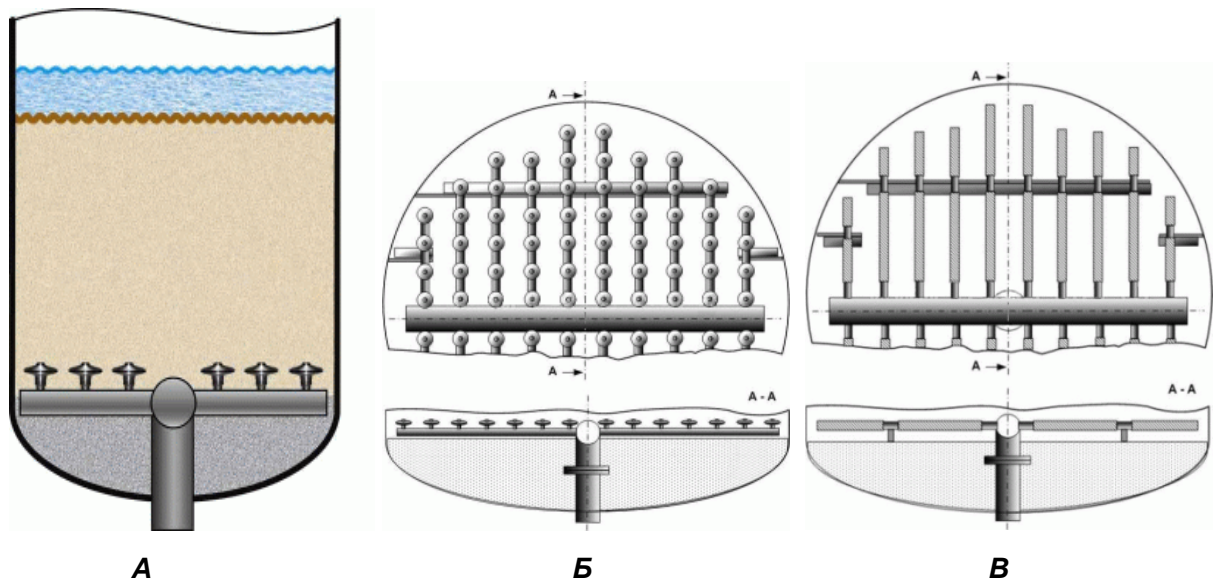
А*- вид фильтра с НРУ на бетонном основании; *Б*- НРУ на бетонном основании с колпачками; *В* - НРУ на бетонном основании со спирально-навитыми лучами
